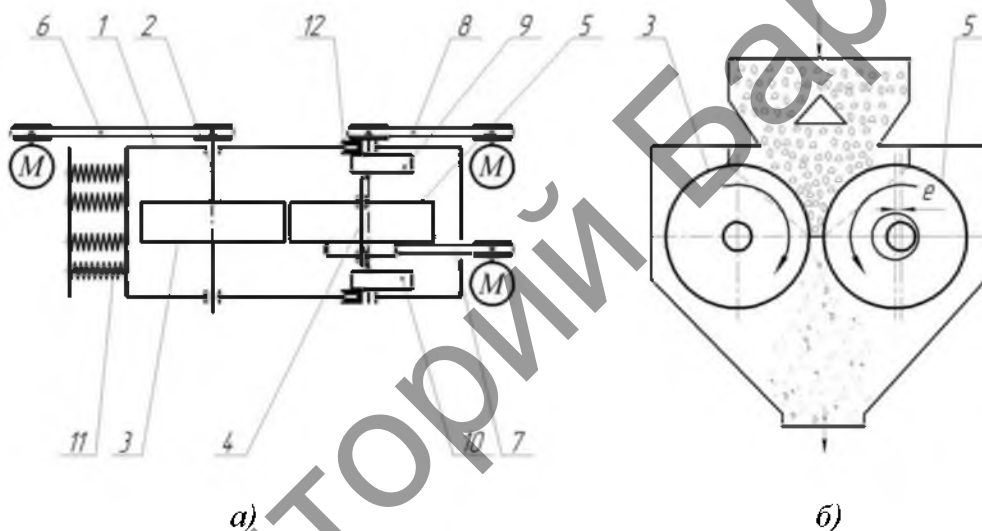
Схема вибровалкового измельчителя-активатора:
